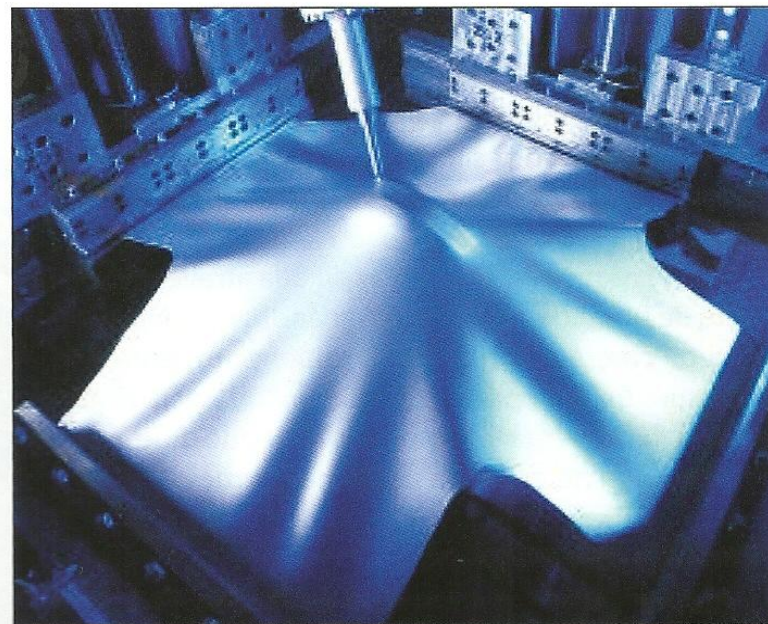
Estampagem incremental. Fonte: Institute of Metal Forming - IBF
